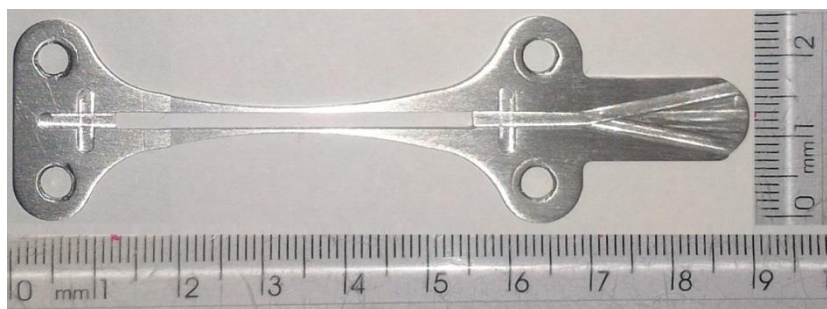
Corpo do sensor em alumínio após a usinagem.
